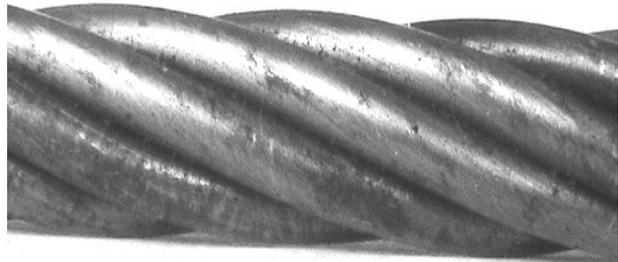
Образец № 3 спиральной свивки диаметром 5 мм изготовленный с неравномерным натяжением проволок
